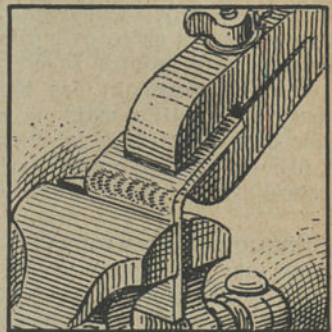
Dobradura do avêso da soldadura.
